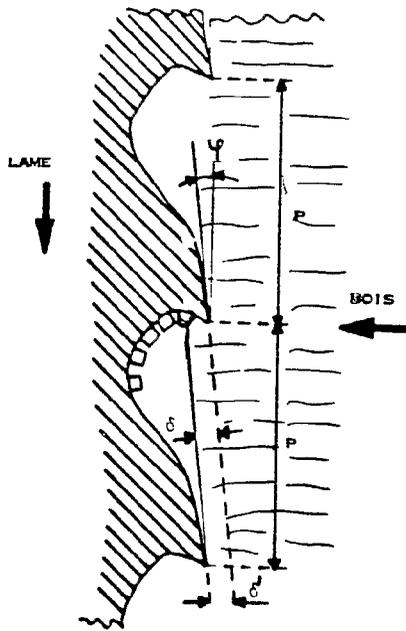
Définition des paramètres géométriques caractérisant la denture.
